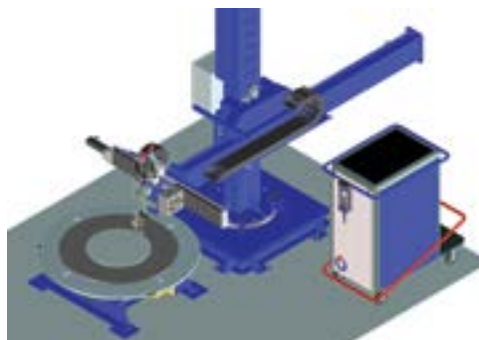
Схема установки для наплавки неподвижной детали в нижнем положении
